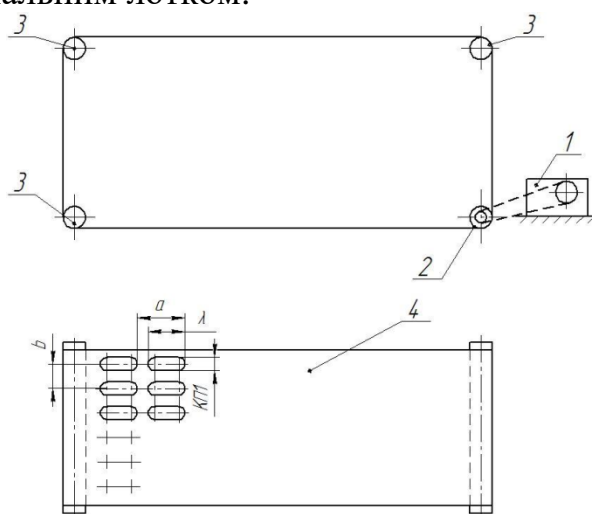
Схема встановлення калібрувального полотна з розмірами комірок: 1 – привід; 2 – ведучий барабан; 3 – підтримувальний барабан; 4 – транспортерна стрічка.
